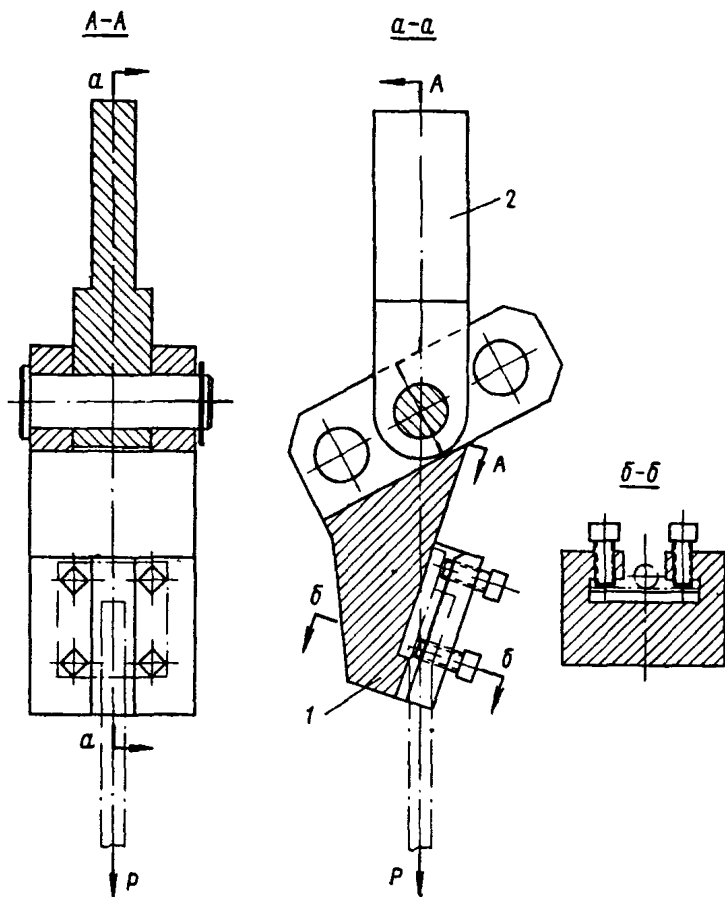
Конструктивная схема приспособления для определения прочности образцов сварных нахлесточных соединений арматурных стержней с пластинами
